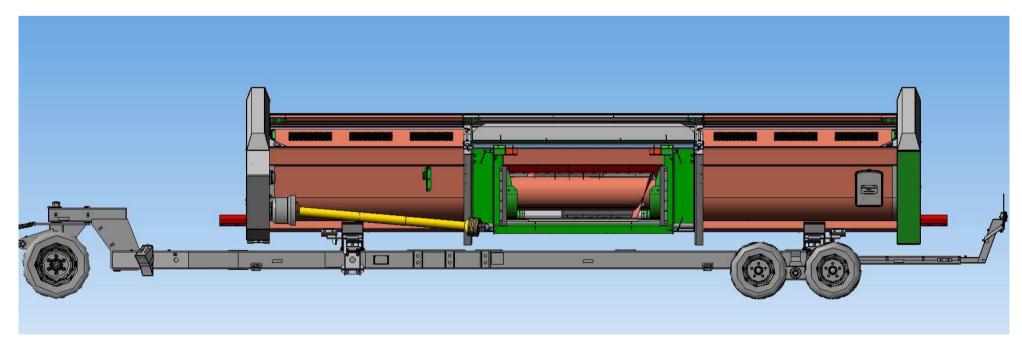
Приспособление для перемещения адаптеров ППА-4000 "Uni Cart 4000" с установленной жаткой RSM SS-560, RSM SS-650. Вид снизу
